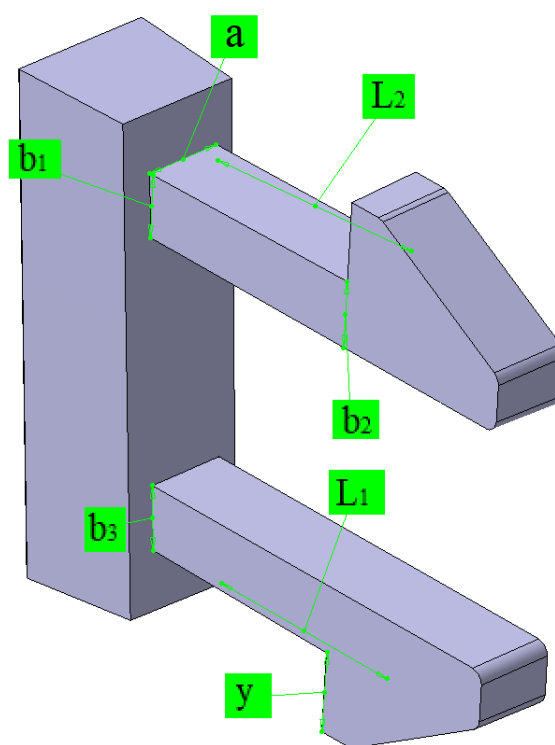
Zavazbení soustavy pomocí Pravidla 3-2-1 – koncept konstrukčního řešení 2.
